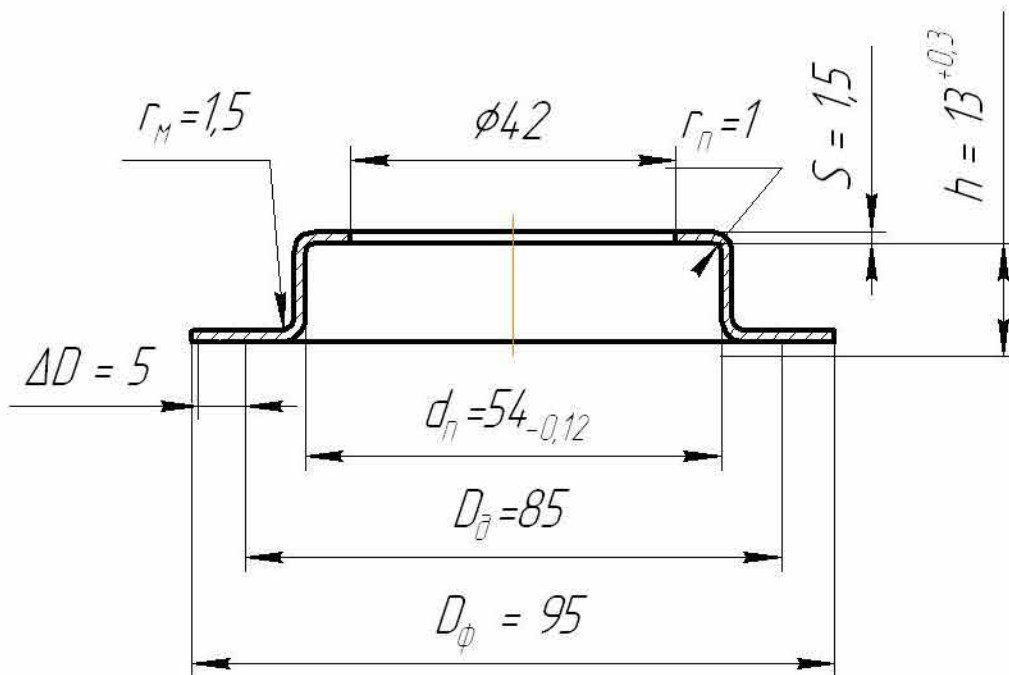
До розрахунку діаметру вихідної заготовки.
